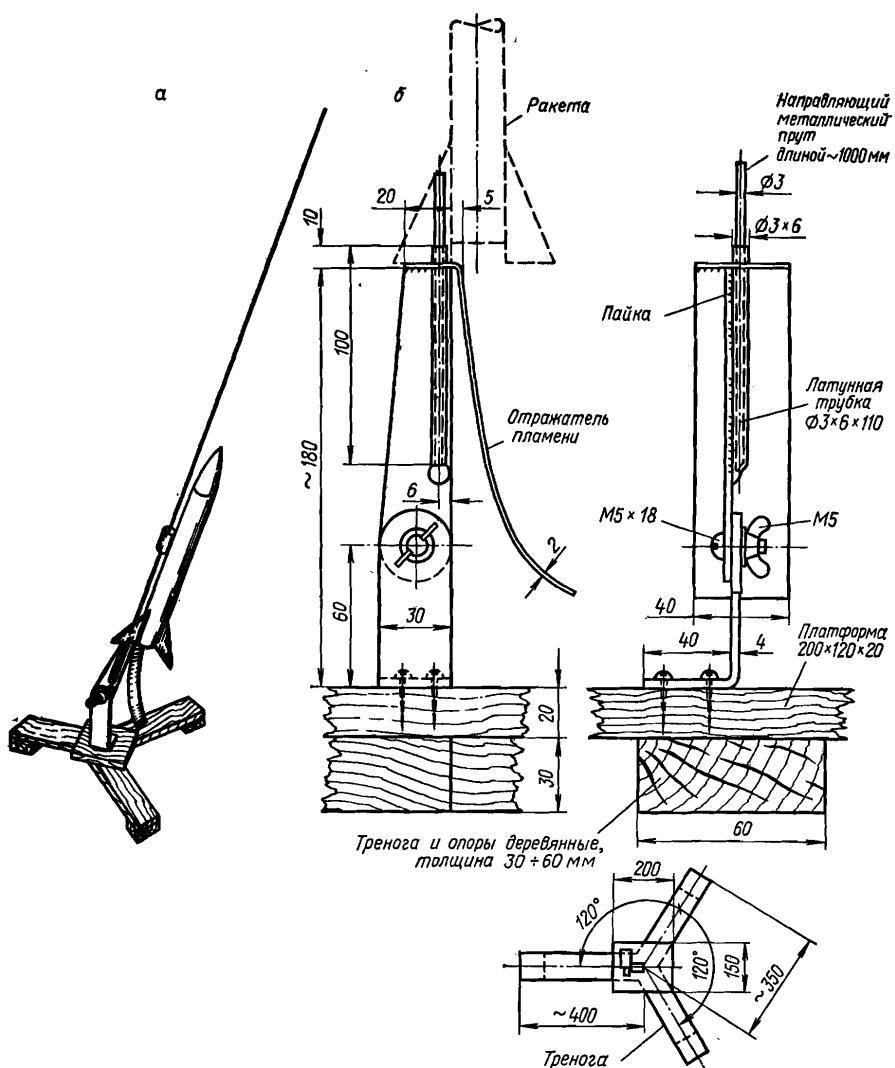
Пусковая установка с прутковой направляющей и регулированием угла запуска.
